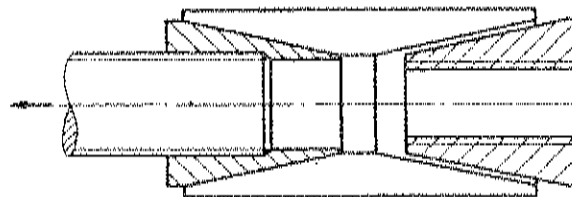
Das Entspannen eines evtl. klemmenden vorderen Druckringes erfolgt in ähnlicher Weise. Nach dem Entfernen der drei farbigen Schrauben sind die Demontage-Hilfsgewinde des vorderen Druckringes zugänglich. Über entsprechende Schrauben kann der vordere Druckring gelöst sowie ein tief in einer Nabenbohrung angeordneter Spannsatz herausgezogen werden.
